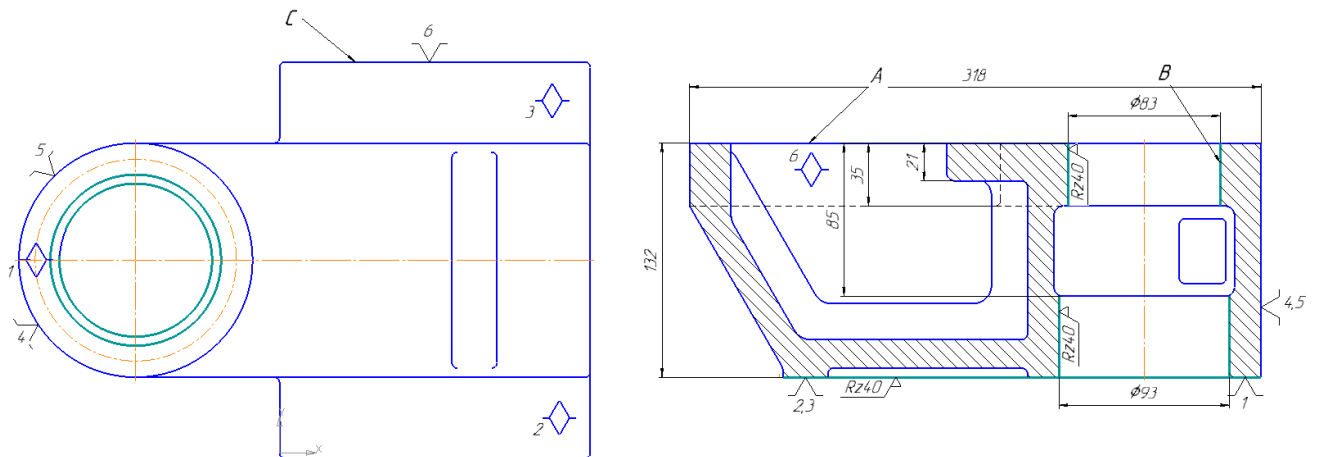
Схема базування та закріплення заготовки на операції 015 фрезерно-розточувальна
